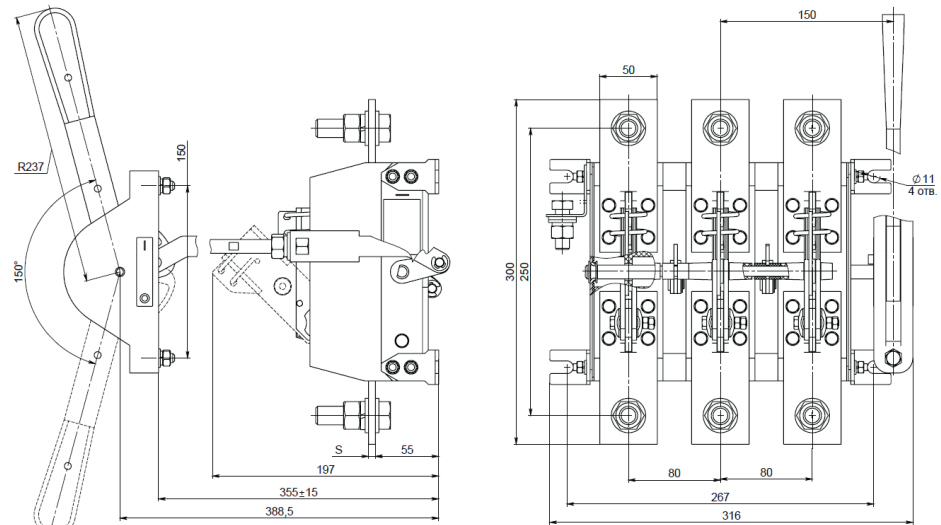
Разъединитель РЕ19–41(43)–32220–00 УХЛЗ с боковой рукояткой, заднего присоединения шин
